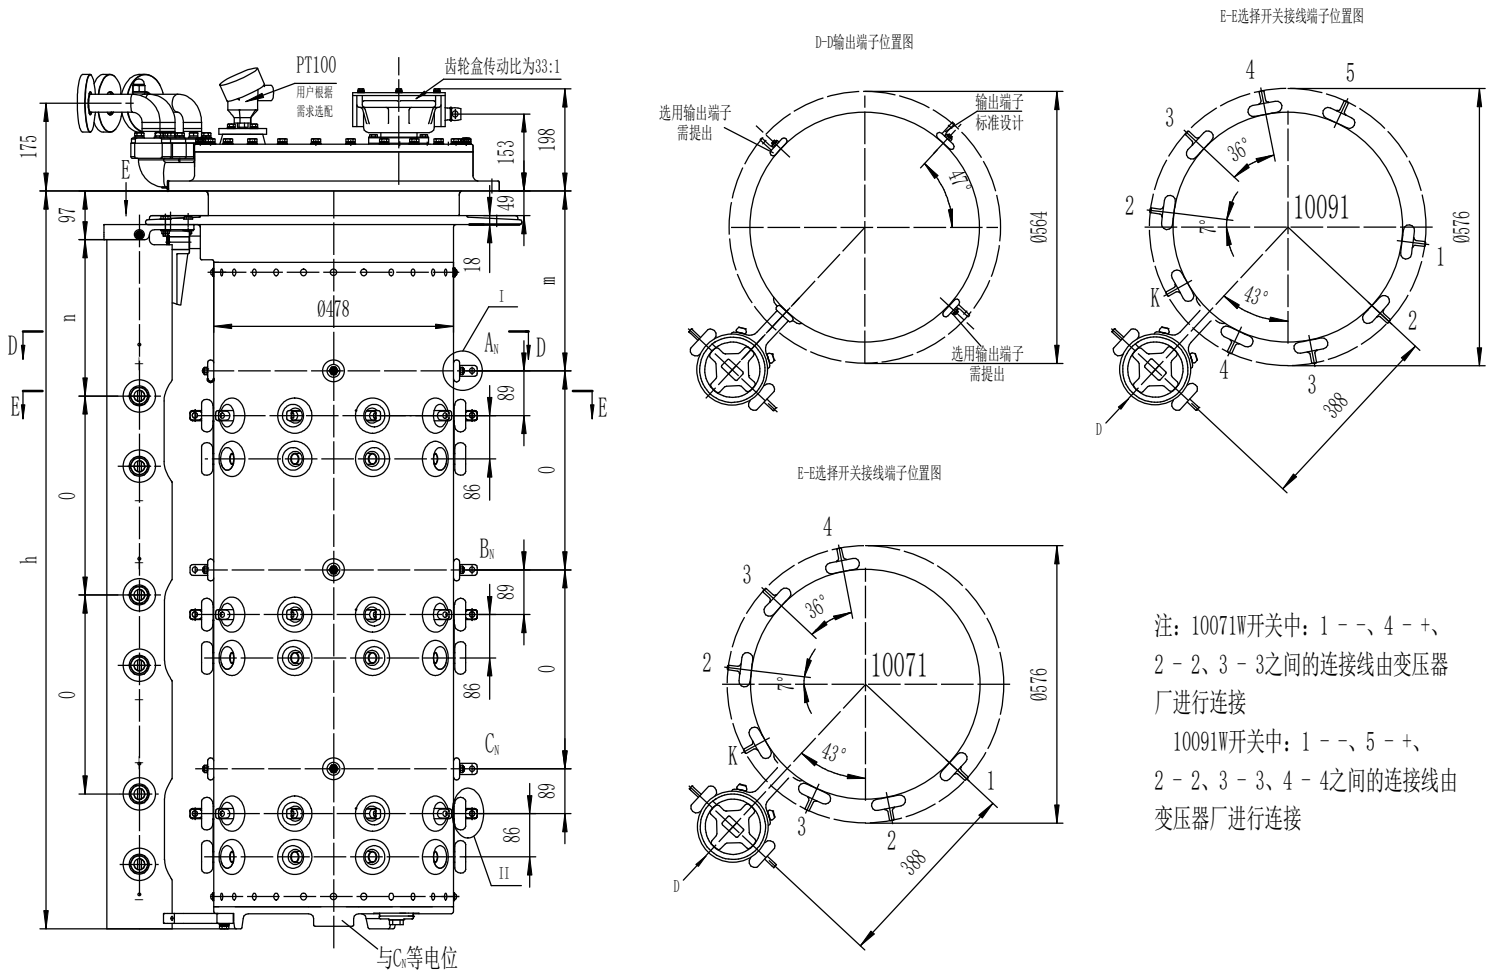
ZVD I 350/500/600带转换选择器外形尺寸图
